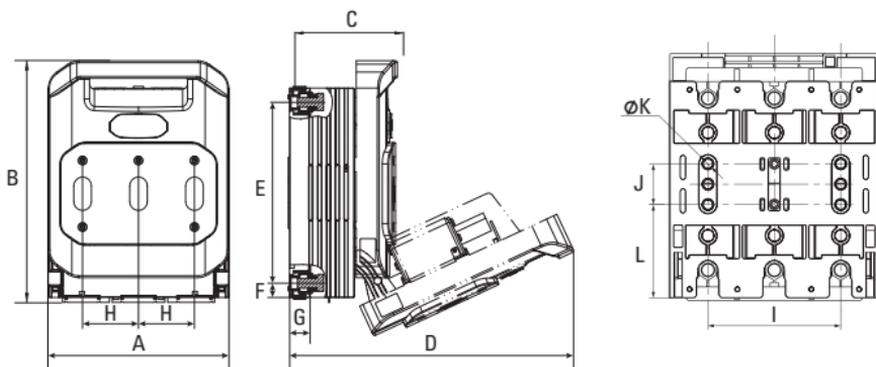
Габаритные размеры выключателя-разъединителя УВРЭ v2 250-630 А ЕКФ
